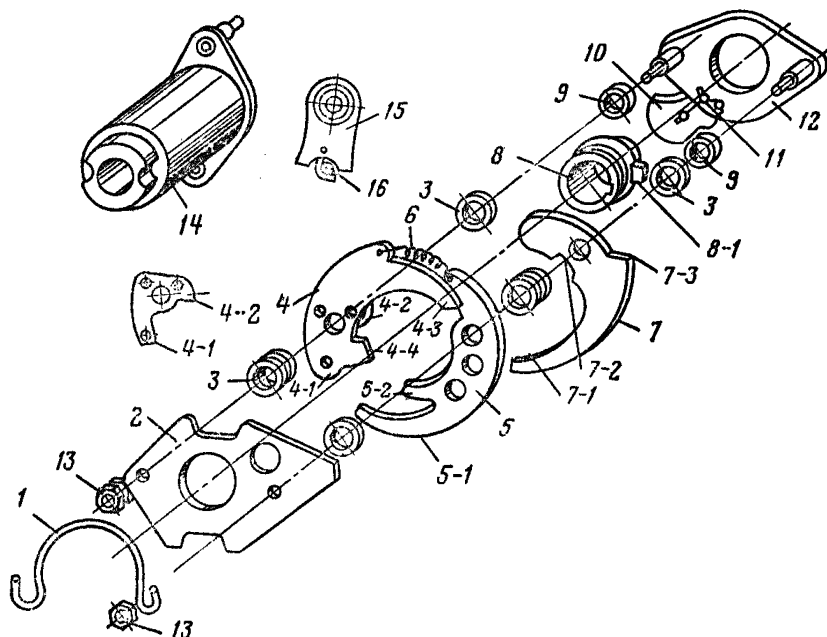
Детализовка механизма свободного расцепления привода ПРА-10;
